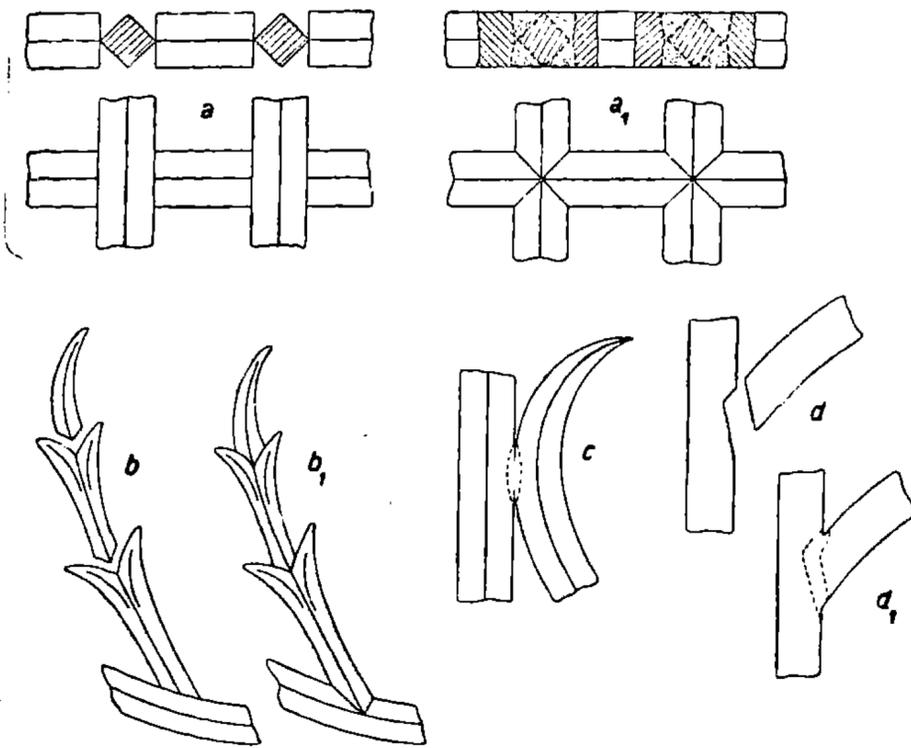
Die Schmelzschweißung als technisch vollkommene und geschmackvollste Ausführungsform feingegliederteter Stabverbindungen.
